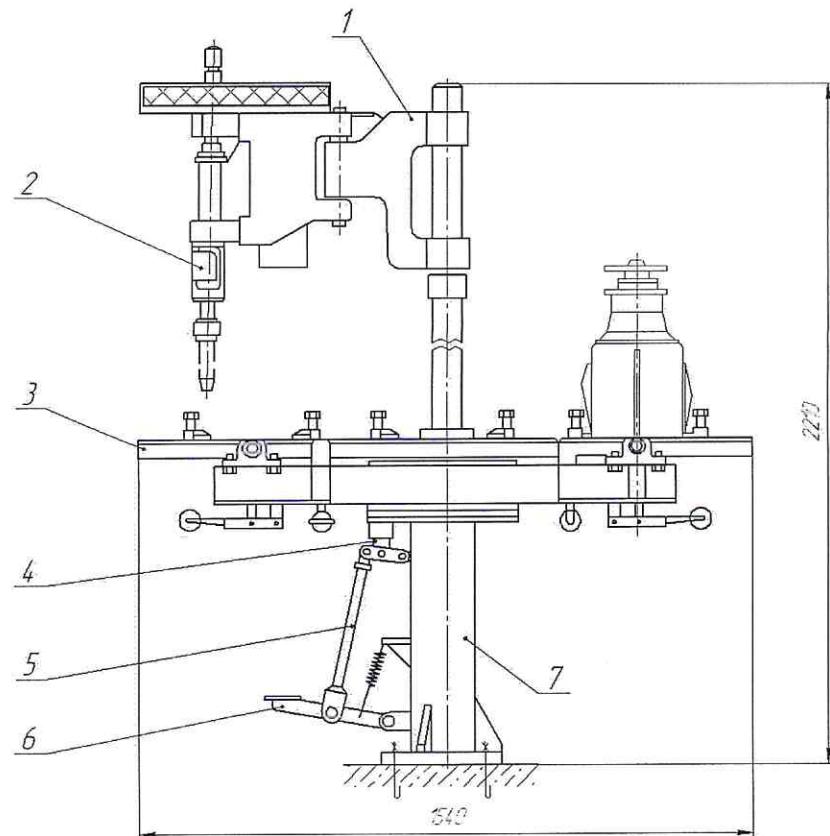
Схема стенда модели 6305-43 для разборки редукторов задних мостов: 1-двуихшарнирная консоль; 2-гайковерт; 3-поворотный стол; 4-стопор; 5-тяга; 6-педаль; 7-стойка.
